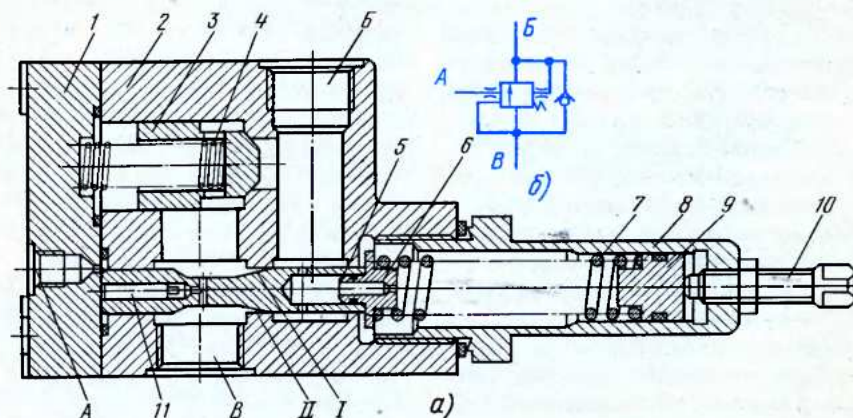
Тормозной гидроклапан с комбинированным управлением запорно-регулирующим элементом золотникового типа (а) и его обозначение на схемах (б):
